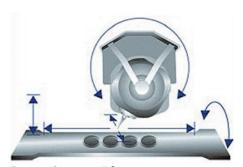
Схема осей движения инструмента фрезеровального центра (Everest)
